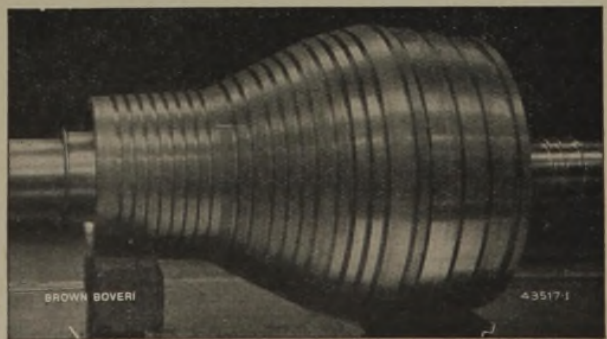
BBC-Elektroschweißung, fertig bearbeitete und geschweißte Turbinentrommel (Werkfoto BBC)
